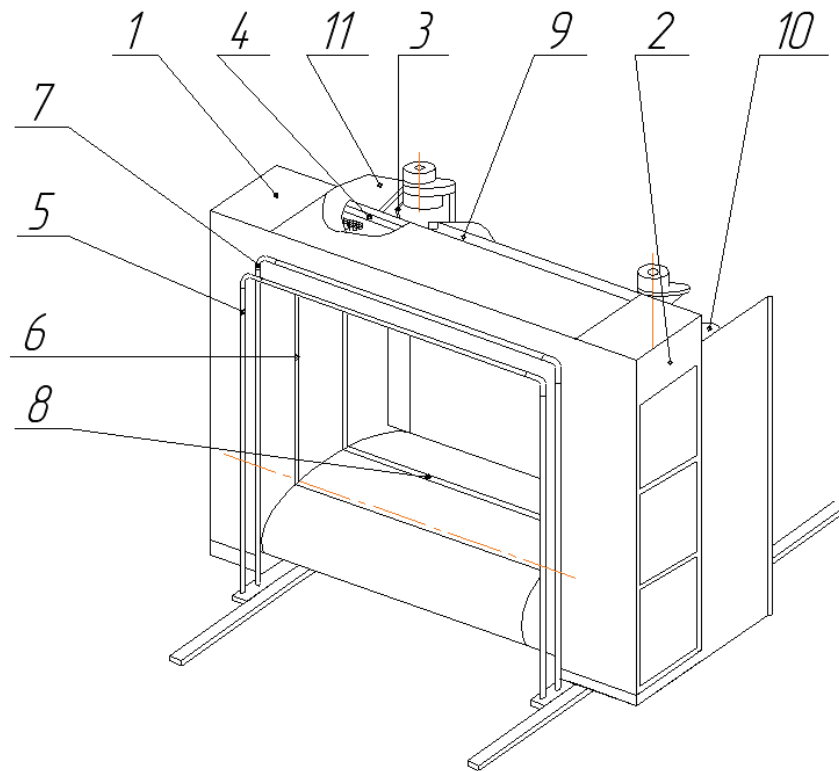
Мийна машина: 1 – арка порталу ліва; 2 – арка порталу права; 3 – консольний кронштейн; 4 – з'єднувальна арка; 5, 6, 7– Система розбризкування; 8 – щітка очистки днища машин; 9, 10 – бокові щітки; 11, 12 – елементи захисту рухомих частин конструкції.
